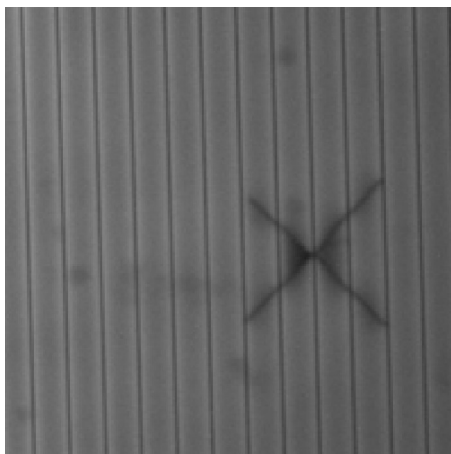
Metalizace zadní strany prosvítající na přední stranu [10]
